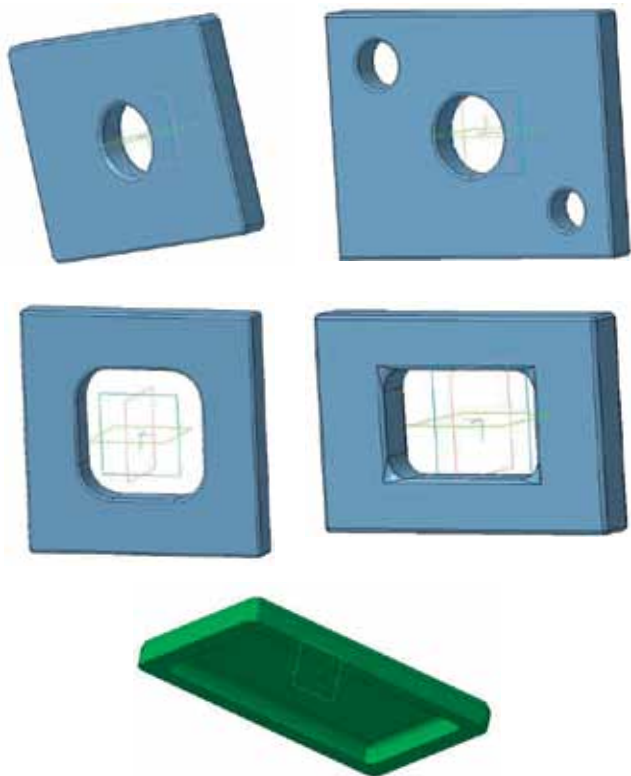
Типовые элементы станины и коробки скоростей токарного станка. Серым цветом помечены отливки из чугуна. Зеленый цвет – крышка из пластика (подлежит распечатке на 3D-принтере)
